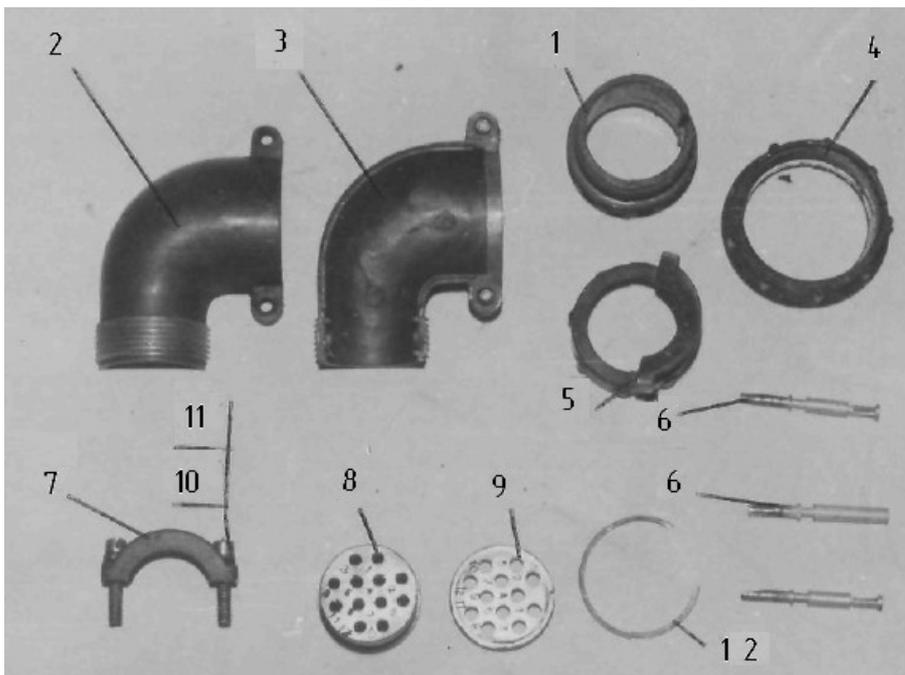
Составные части разъема: 1. Корпус; 2. Крышка; 3. Крышка; 4. Гайка накидная; 5. Гайка; 6. Контакт; 7. Прижим; 8. Изолятор; 9. Кондуктор; 10. Винт; 11. Шайба; 12. Кольцо стопорное.
